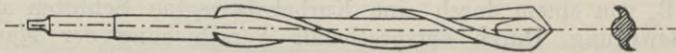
Schrämwerkzeug mit schraubenförmig verlaufenden Schneiden.
